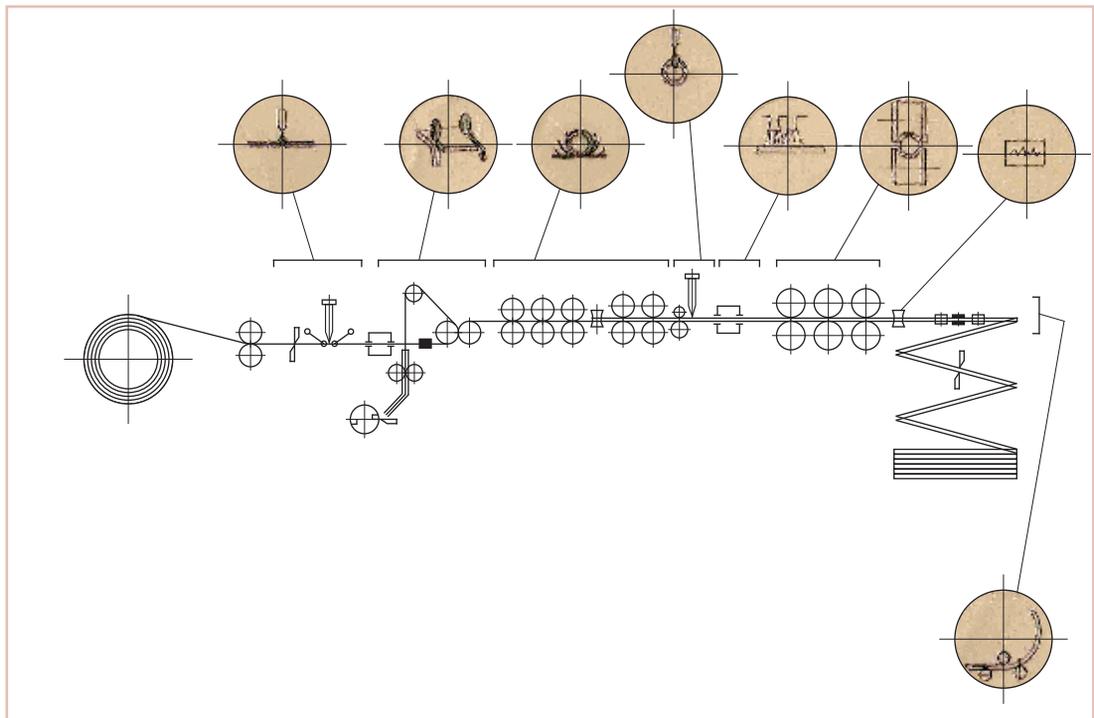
По-операционная схема формовки сварной трубной заготовки
